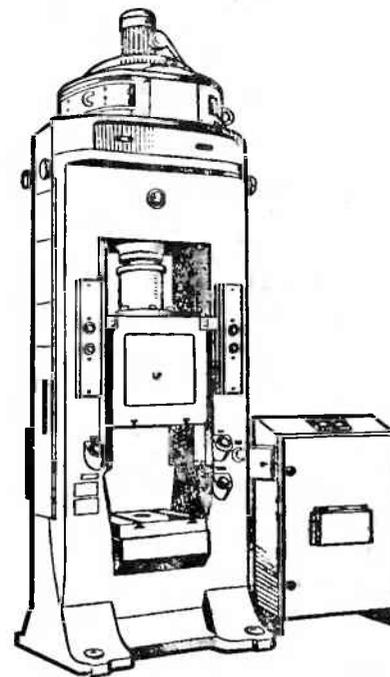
Винтовой пресс с дугостаторным приводом усилием 160 тс
